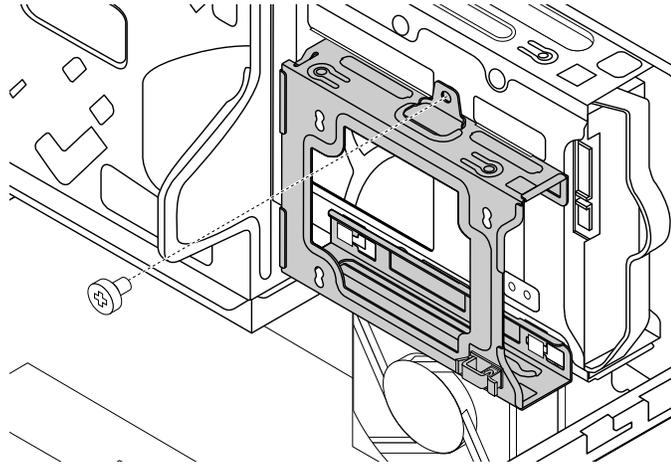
Die Schraube anbringen, mit der die Halterung des sekundären Festplattenlaufwerks befestigt wird
